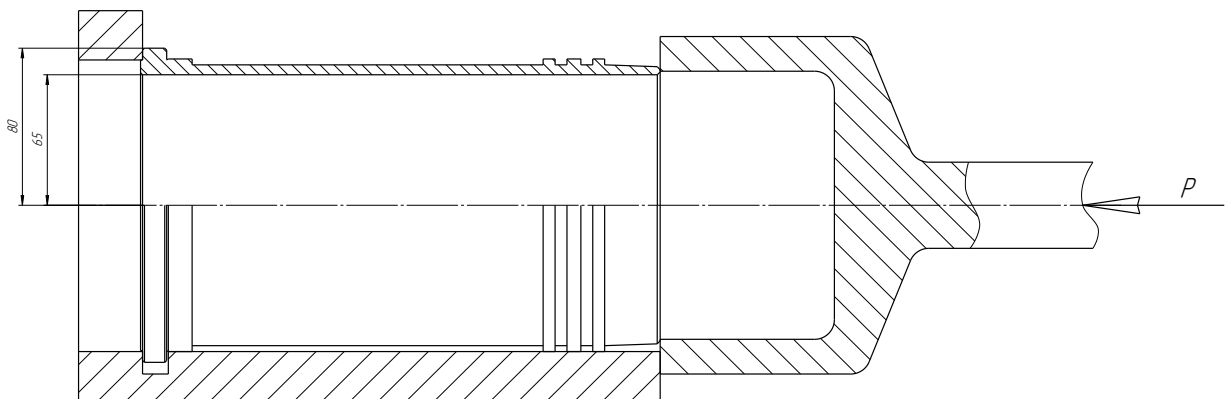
Схема пневматичного затискаючого пристрою
